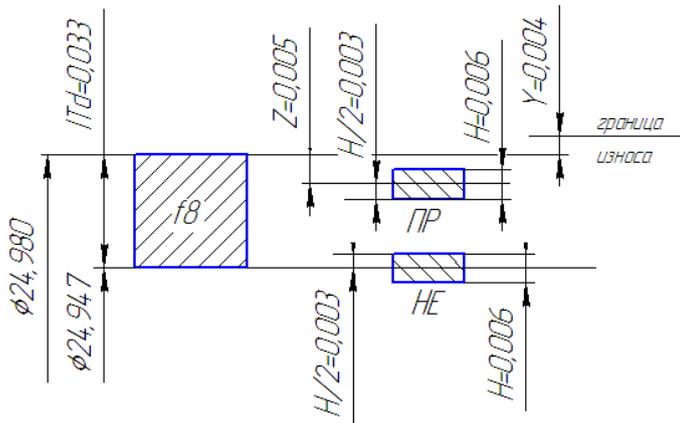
Схемы расположения полей допусков калибра-скобы.
